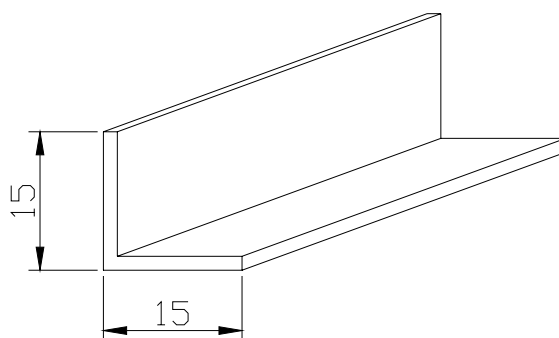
Pieza con las dimensiones que se quieren conseguir mediante el plegado
